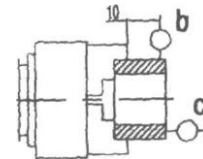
Токарный патрон с креплением заготовки за внешнюю поверхность с обратными кулачками
